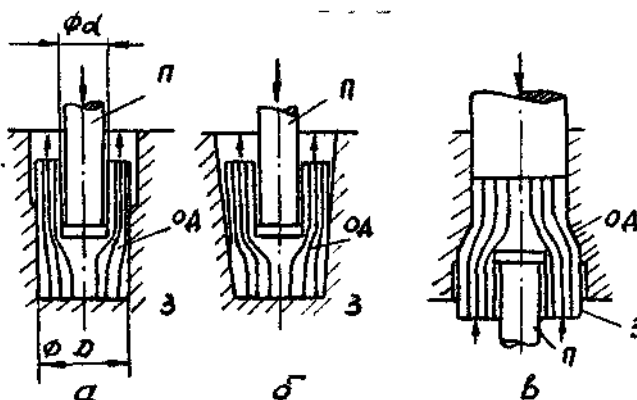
Способы закрытой прошивки, а, б – обратные схемы; в – прямая схема
